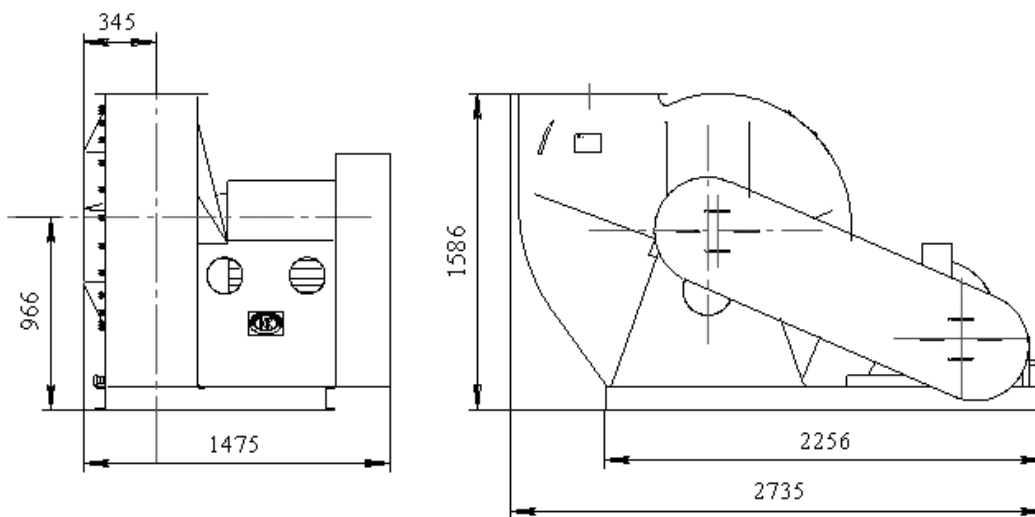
Вентиляторы ВРП-100-45-10. Габаритные размеры
